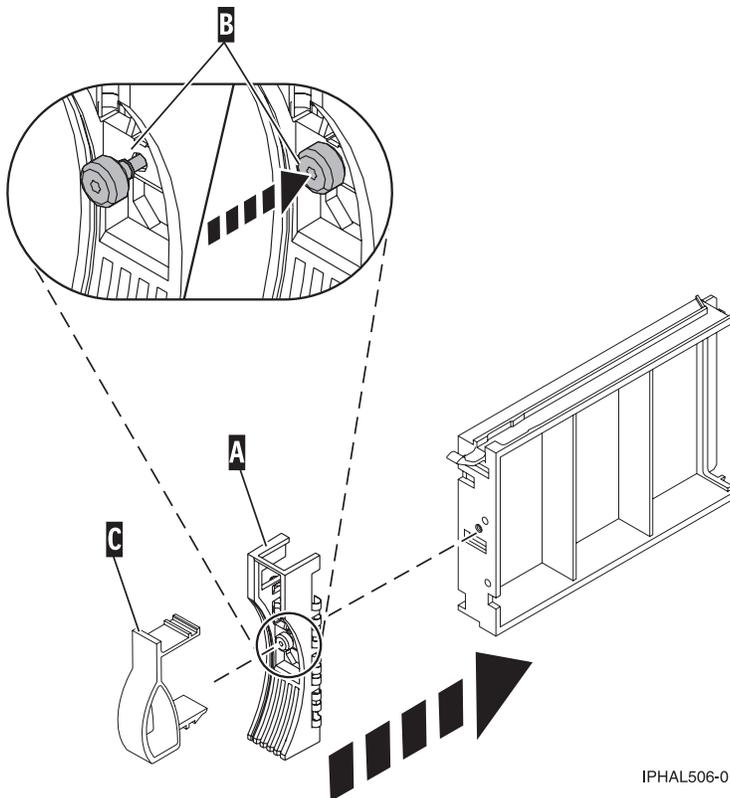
Fixation d'un panneau frontal à un obturateur d'unité de disque
